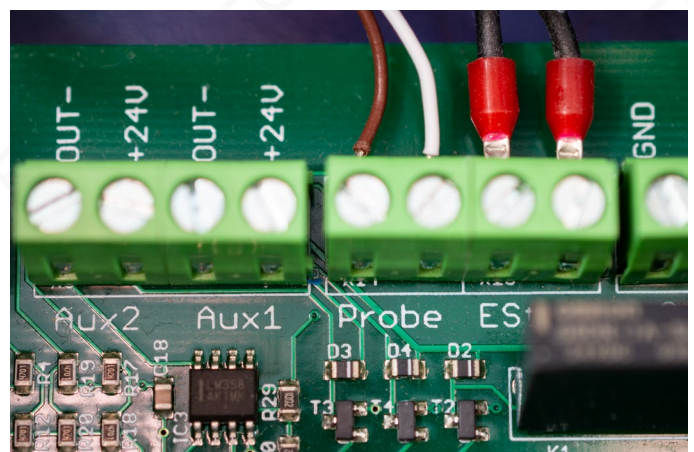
Anschluss des Werkzeiglängensensors, hier mit brauner und weißer Ader
